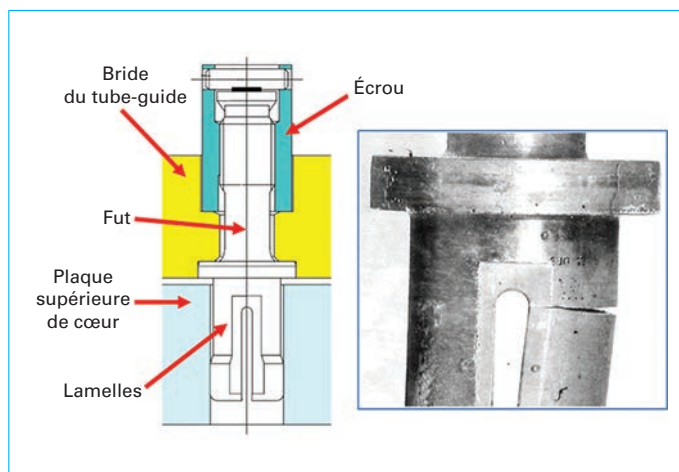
Schéma d'une broche de tube-guide : fissuration au niveau d'une lamelle
